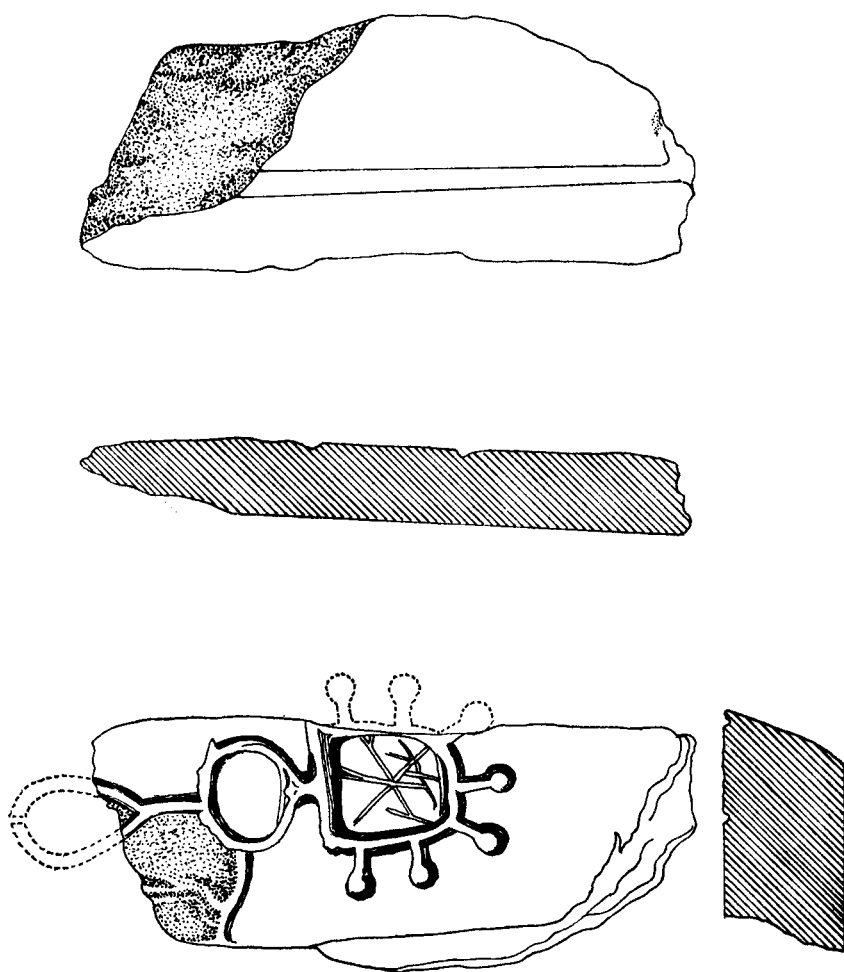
Molde para fundição de brincos (comp. 75 mm)
